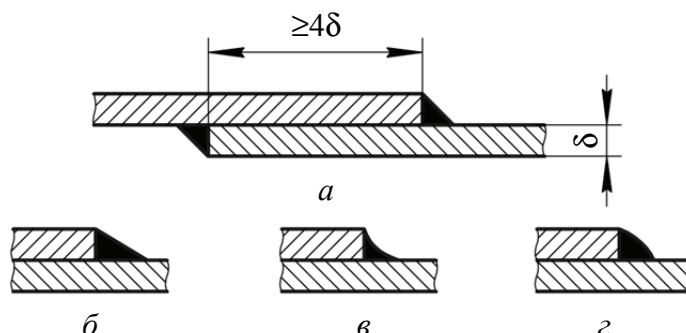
Сварное нахлесточное соединение:
